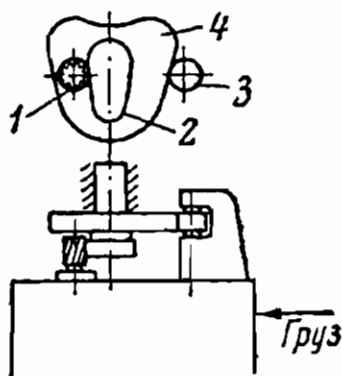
Приспособление для фрезерования кулачков на горизонтально-фрезерном станке
